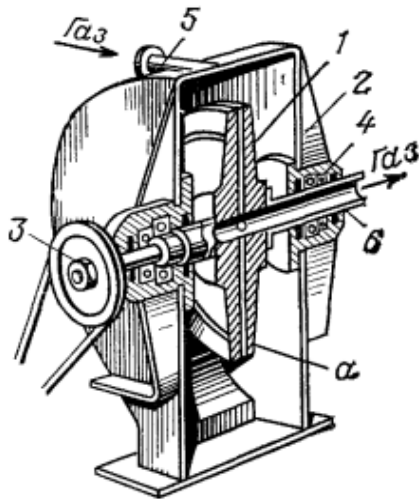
Відцентровий пиловловлювач ЦРП: 1 – ротор; 2 – корпус; 3 – шків; 4 – опора; 5 – патрубок; 6 – полий вал; *a* – радіальний канал
